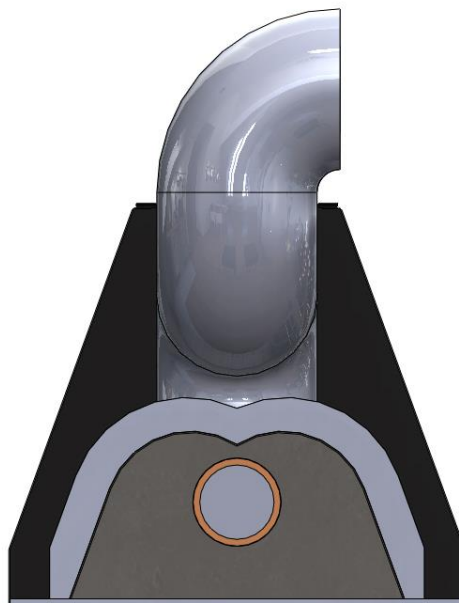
Sección transversal del concentrador secundario. Fuente: Propia
